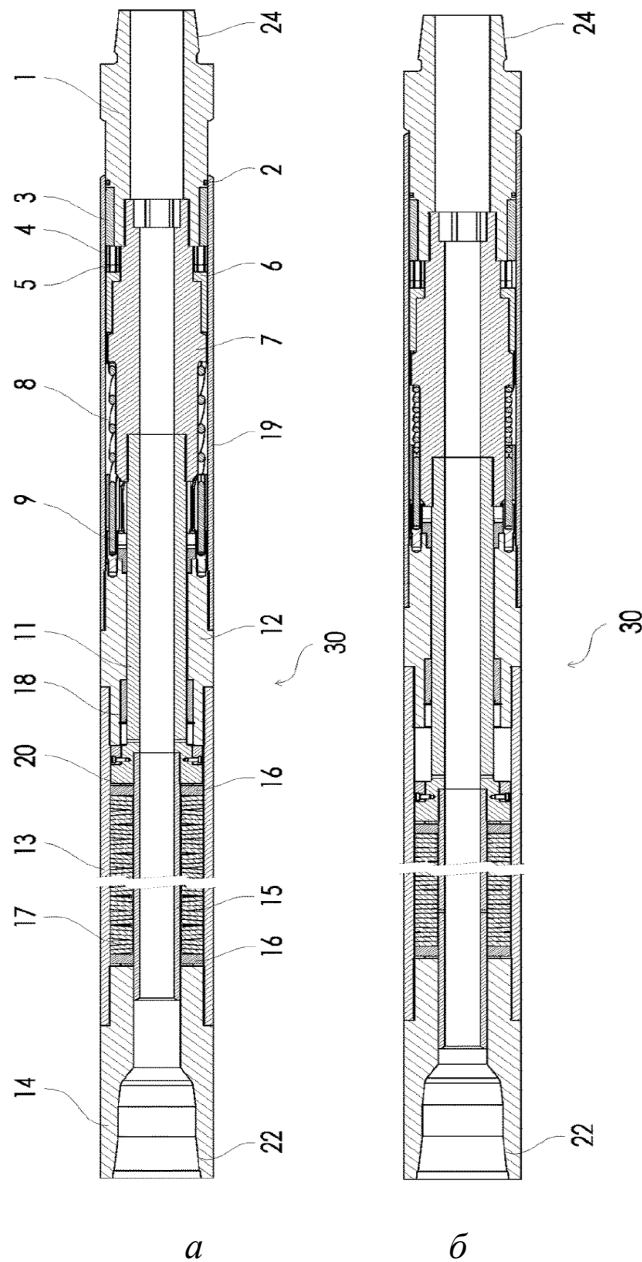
Принцип роботи Torque and Torsion Limiting Tool: а – розширений стан, б – стиснутий стан [42].
